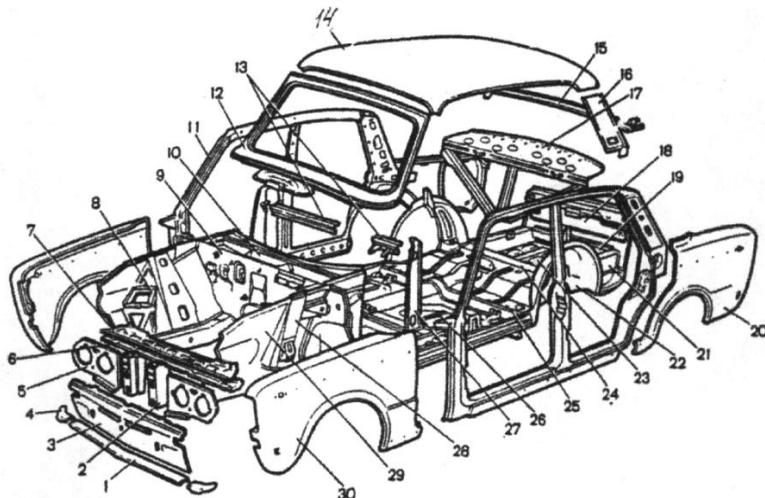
Детали остова кузова: 1-брызговик передка центральный; 2-стойка передка; 3-панель передка нижняя; 4-брызговик переднего бампера правый; 5-кожух фары; 6-поперечина передка верхняя; 7-усилитель верхней поперечины; 8-площадка аккумулятора; 9-щиток передка; 10-коробка воздухопритока; 11-боковина; 12-панель рамы ветрового окна; 13-нижняя поперечина панели приборов; 14-панель крышки; 15-панель рамы заднего окна; 16-боковая панель крышки; 17-рамка задней перегородки с полкой; 18-панель задка; 19-нижняя поперечина задка; 20-заднее крыло; 21-лонжерон пола задка; 22-арка заднего колеса; 23-пол багажника; 24-поперечина пола багажника; 25-задняя поперечина пола; 26-передний пол; 27-усилитель передней стойки; 28-стойка брызговика; 29-брызговик; 30-переднее крыло
